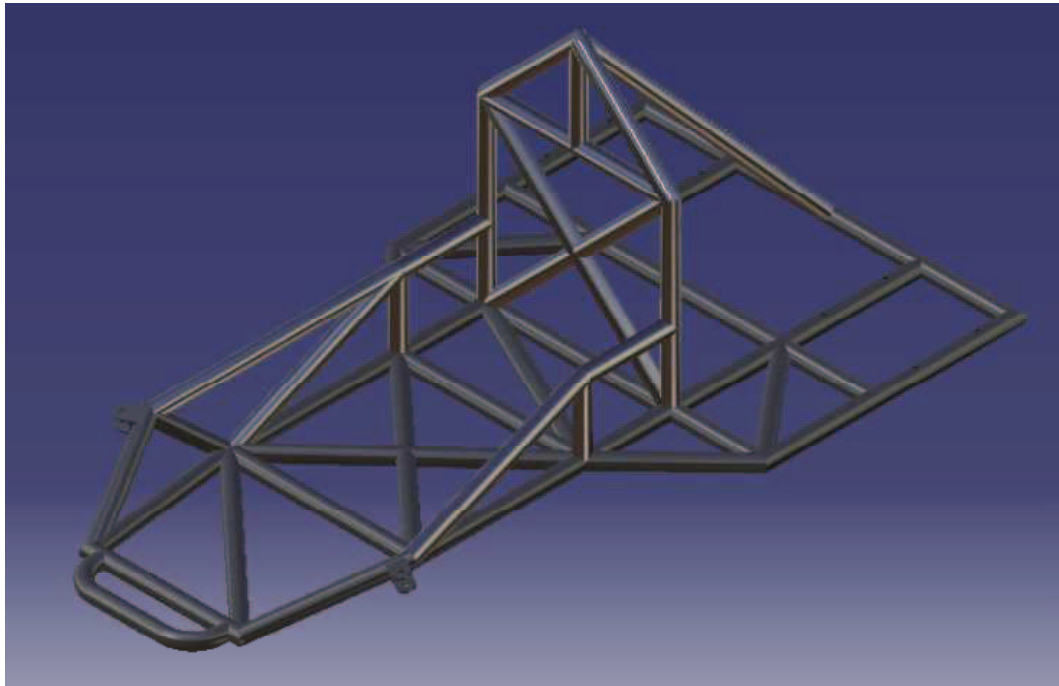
Vista Isométrica del Chasis Tubular.
